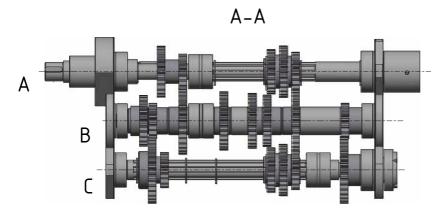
Vorschubgetriebe 2-6 - Feed gear 2-6
